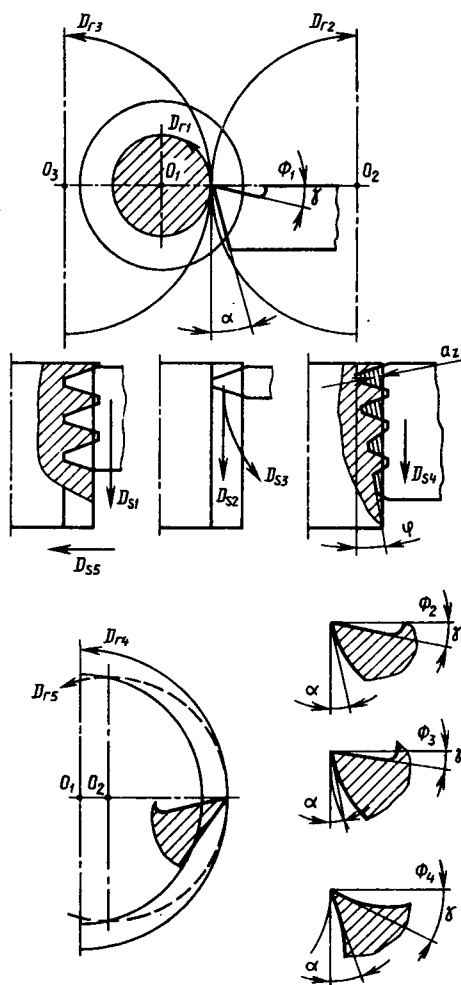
Обобщенная модель образования резьбы резьбонарезным инструментом
